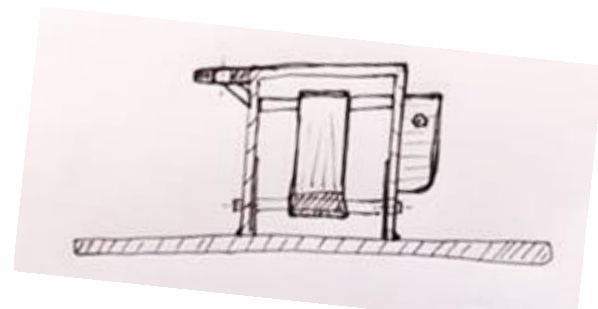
Zijaanzicht rechts plateau en tussenbalk slackline
